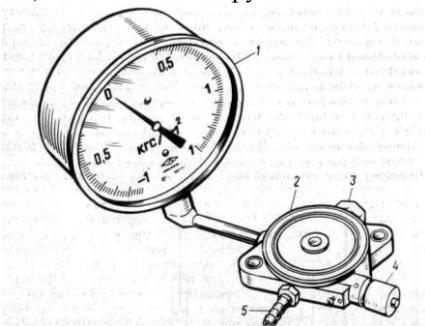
Приспособление для проверки герметичности цистерн: 1 – мановакуумметр; 2 – корпус; 3 – кран управления; 4 – предохранитель; 5 – штуцер для нагнетания воздуха
